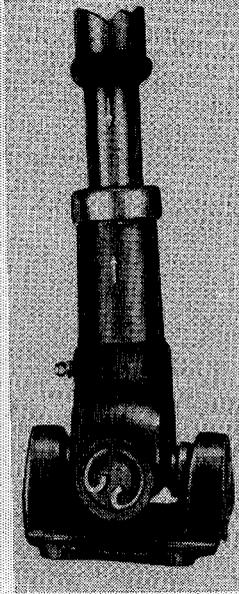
Pfeilmarkierung der Keilwellenverbindungen.
